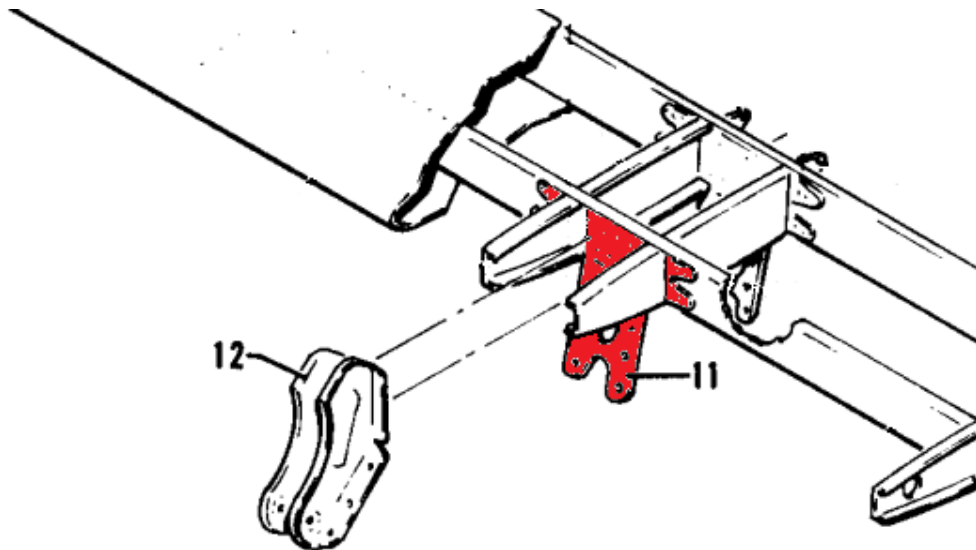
Elevator and Stabilizer Assemblies (Stabilizer attachment Fitting P/N 77615-07)
